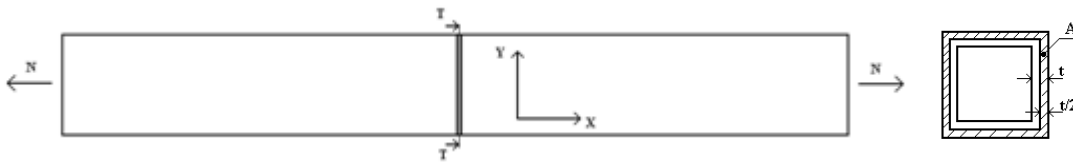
Representação em corte da zona de ligação por soldadura, de um corte a direito
